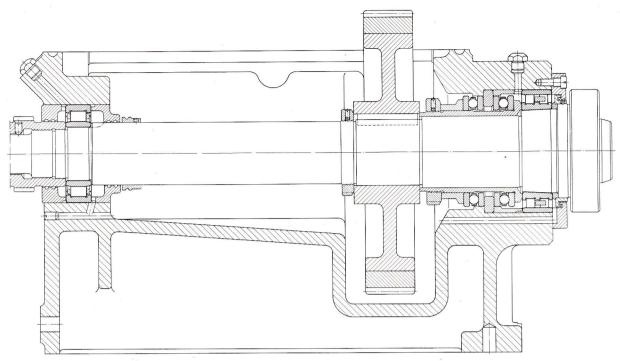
Disposición de rodamientos para el husillo de torno de la fig. 7
